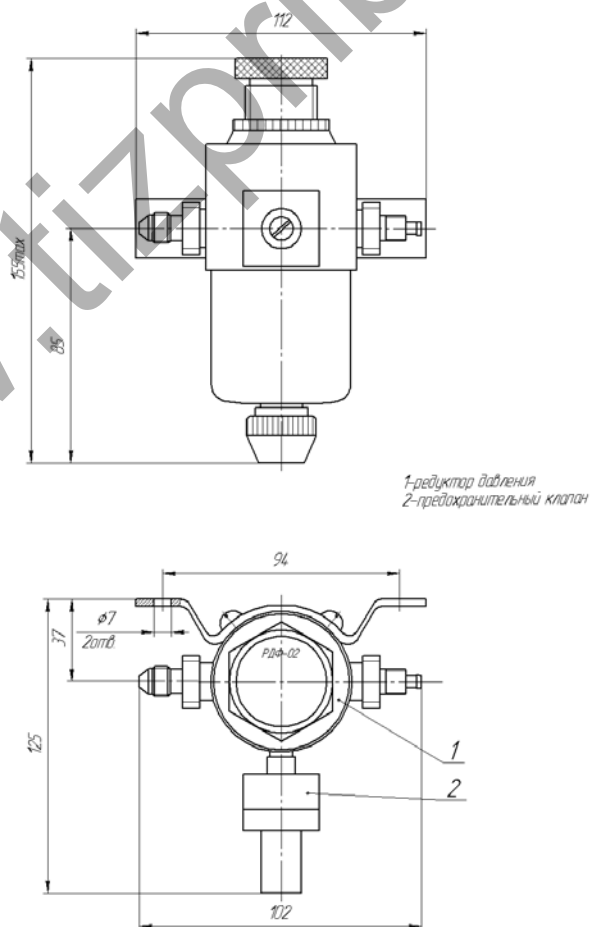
Габаритные и установочные размеры редуктора РДФ-02
